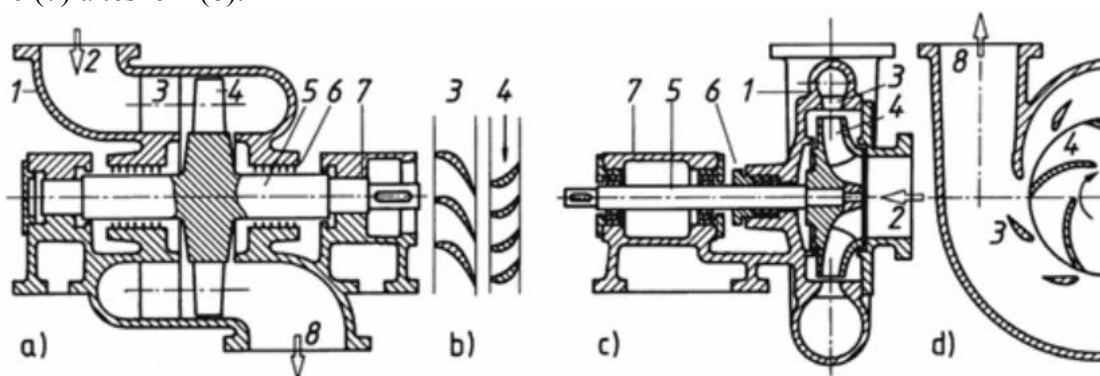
Rozdělení lopatkových strojů podle směru proudění k ose rotace [1]
